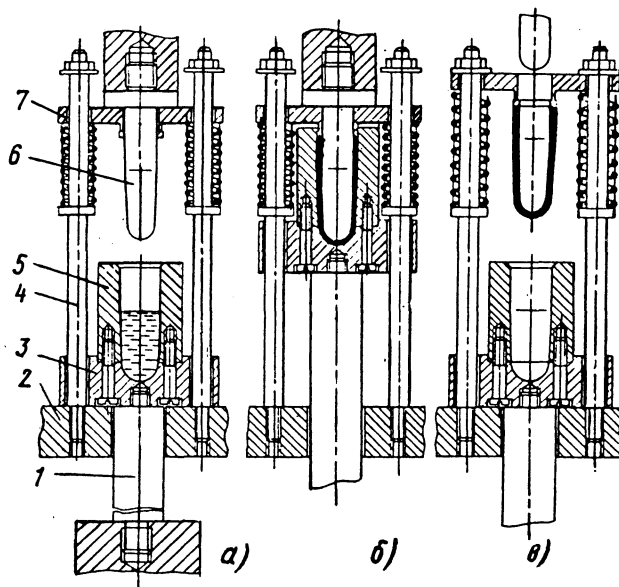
Схема процесса штамповки из жидкого металла тонкостенной детали:
